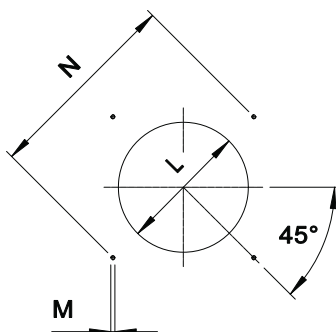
ФЛАНЕЦ ДЛЯ УСТАНОВКИ ГОРЕЛКИ
